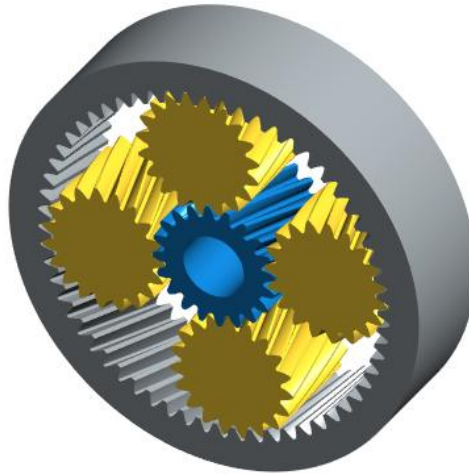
2º estágio; Engrenagens planetárias a amarelo; Engrenagem solar a Azul; Engrenagem anelar a cinzento
